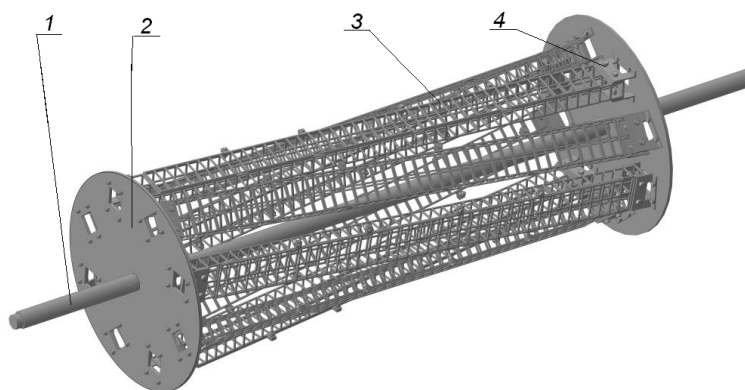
Конструкция многоместного приспособления для обработки детали в свободном состоянии:
